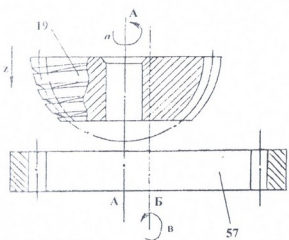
Схема нарезания круглого цилиндрического колеса с внутренними зубьями
